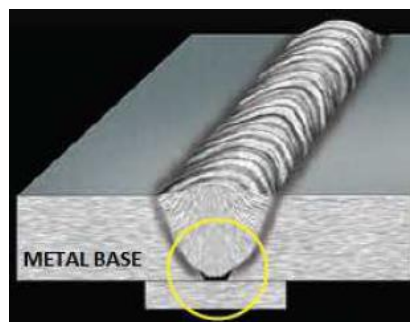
Falta de penetración cordón de soldadura [4].
